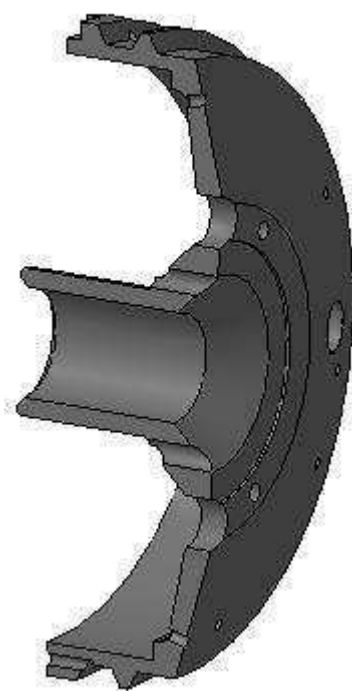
Разрез 3D модели детали "Корпус опоры"
